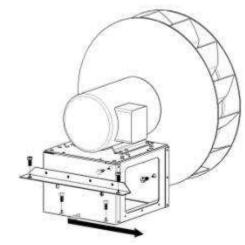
Pernos que conectan el soporte del motor al ventilador
